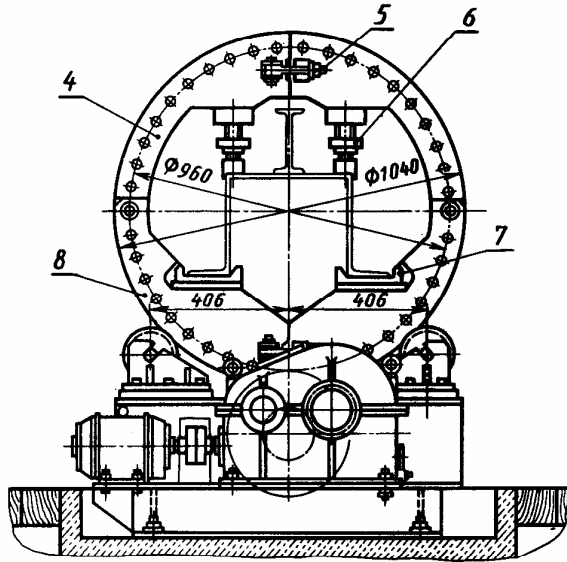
Положения хребтовой балки при сборке и автоматической сварке
